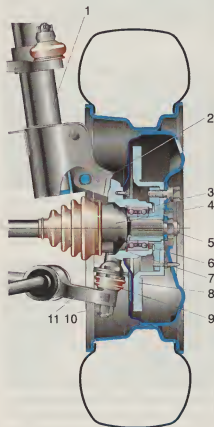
Переднее колесо и близлежащие детали: 1 — телескопическая стойка; 2 — поворотный кулак; 3 — ступица; 4 — наружный ШРУС; 5 — гайка M20x1,5; 6 — подшипник; 7 — стопорное кольцо; 8 — тормозной диск; 9 — шаровой шарнир; 10 — гайка; 11 — рычаг подвески.
